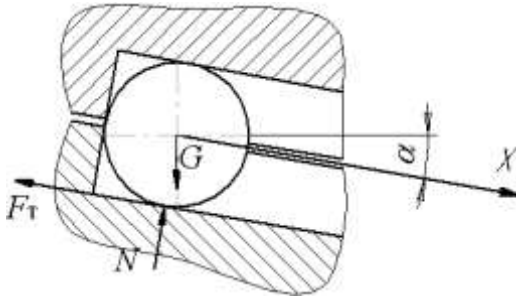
Розрахункова схема початкового стану муфти
